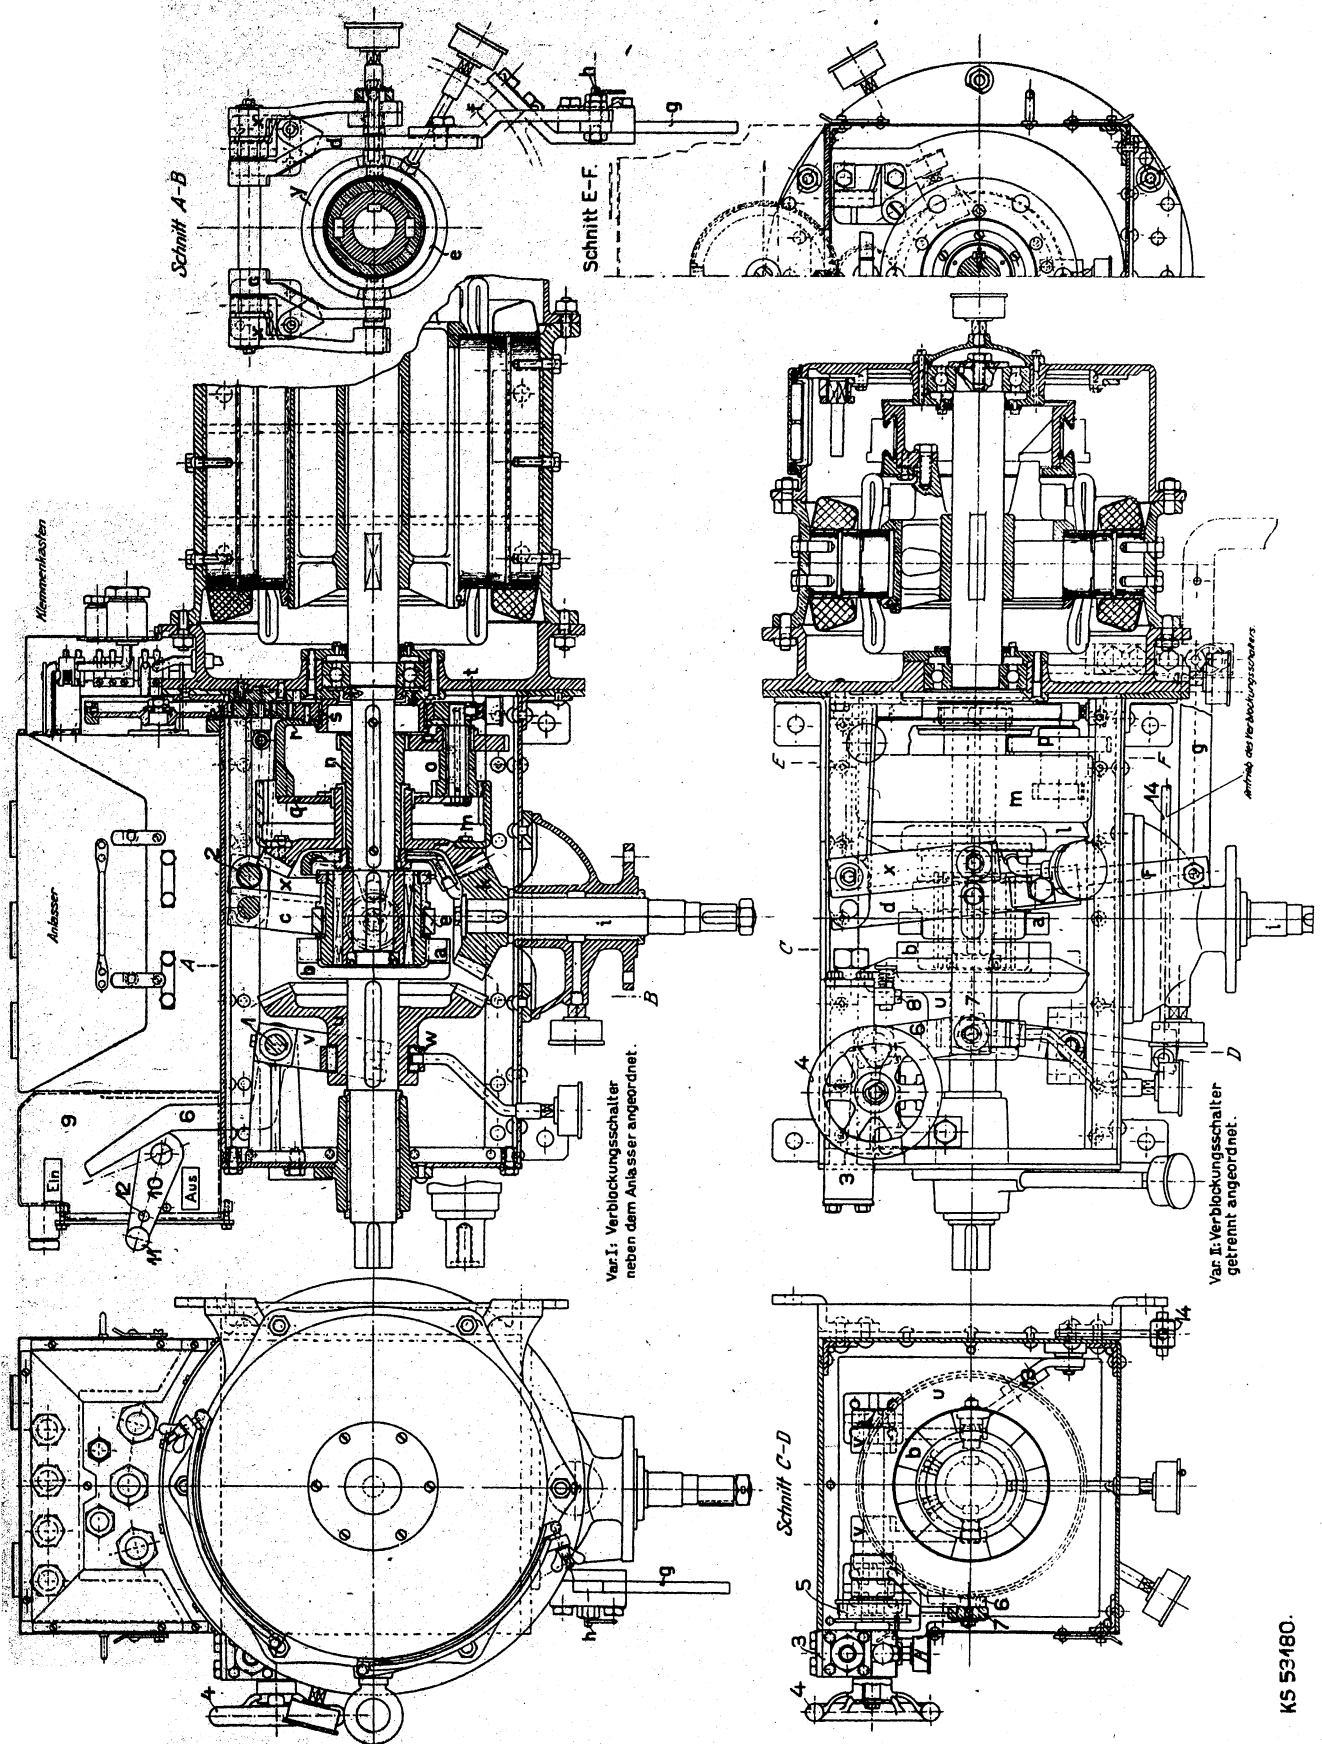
Schnittzeichnung einer liegend ausgeführten Rudermaschine (S. S. W.)
